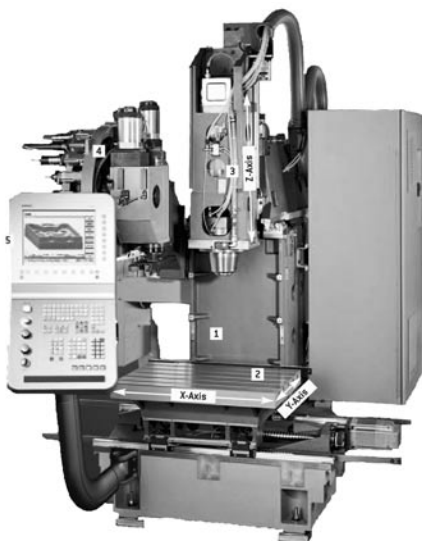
Вертикальный обрабатывающий центр *DMC 635 V eco
